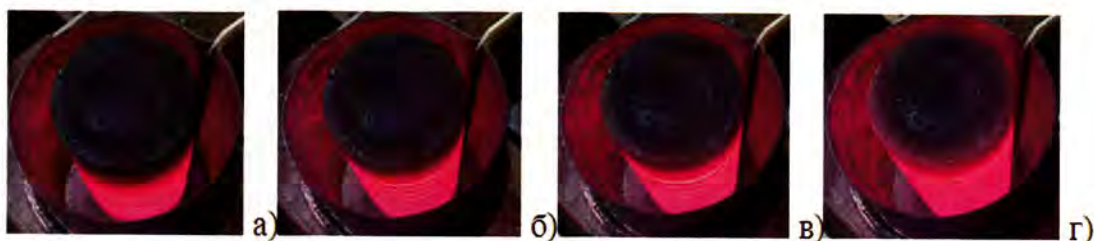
Полосатый нагрев цилиндра из магнитной стали в одновитковом индукторе
